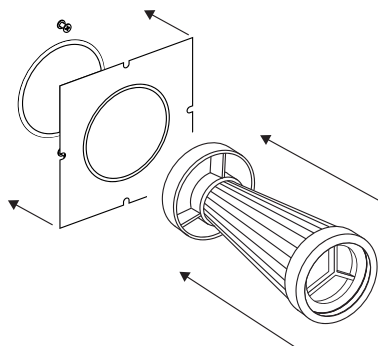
Установка фильтра и уплотнительного элемента
